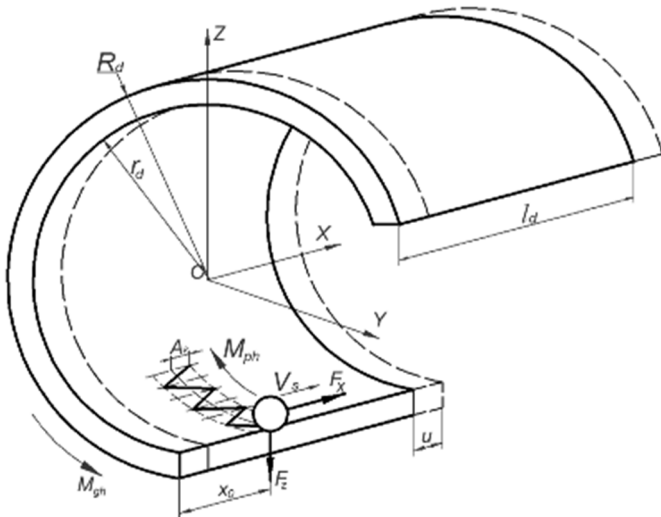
Розрахункова схема для побудови динамічної моделі поздовжнього руху заготовки в процесі формування регулярного мікрорельєфу
